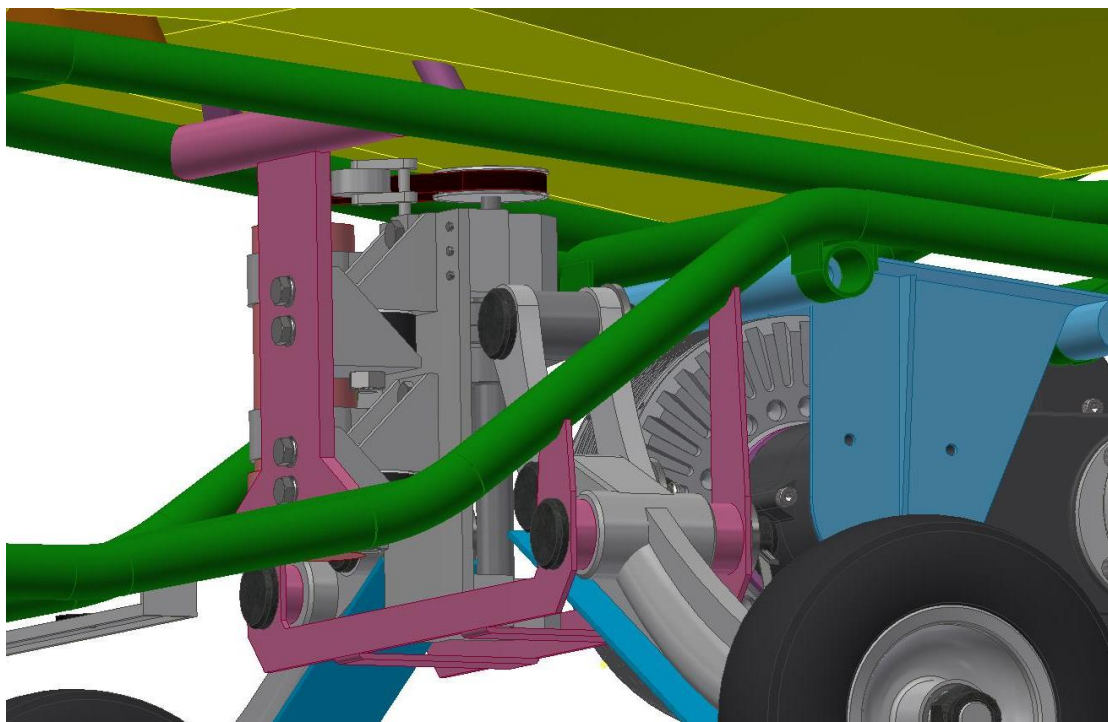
CAD model druhé verze mechanismu – pohled zepředu
